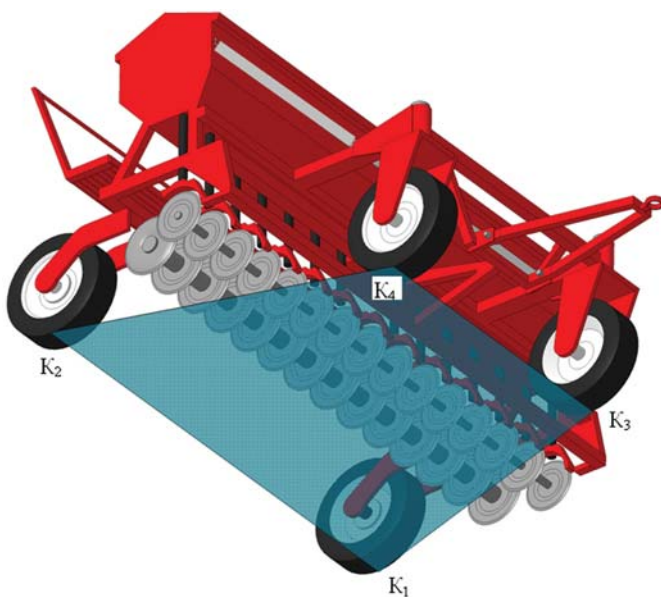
Схема розташування опорного контуру сіялки зернотукової пресової СЗП-3,6В-06
